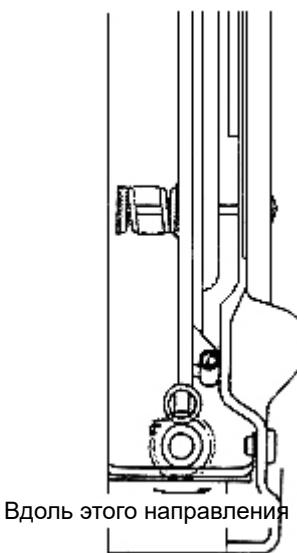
Саморегулирующийся механизм выборки зазора
